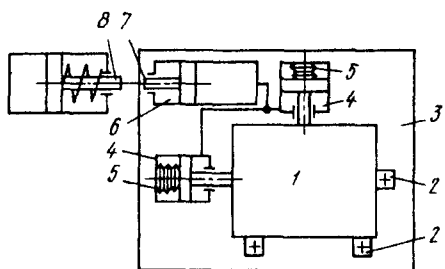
Схема закрепления заготовки на спутнике тарельчатыми пружинами
